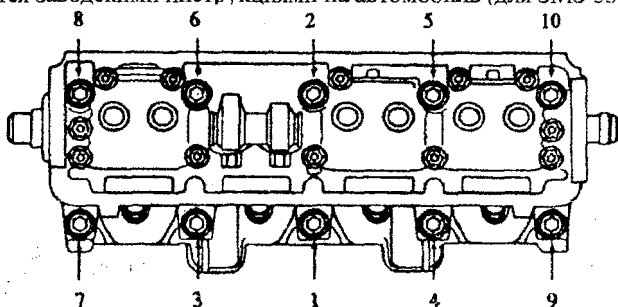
Порядок затягивания болтов крепления головки цилиндров
